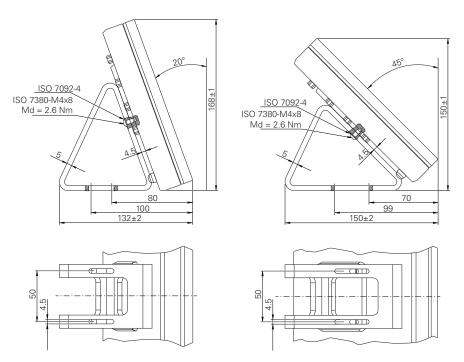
Dimensões do aparelho com pé de suporte Duo-Pos
